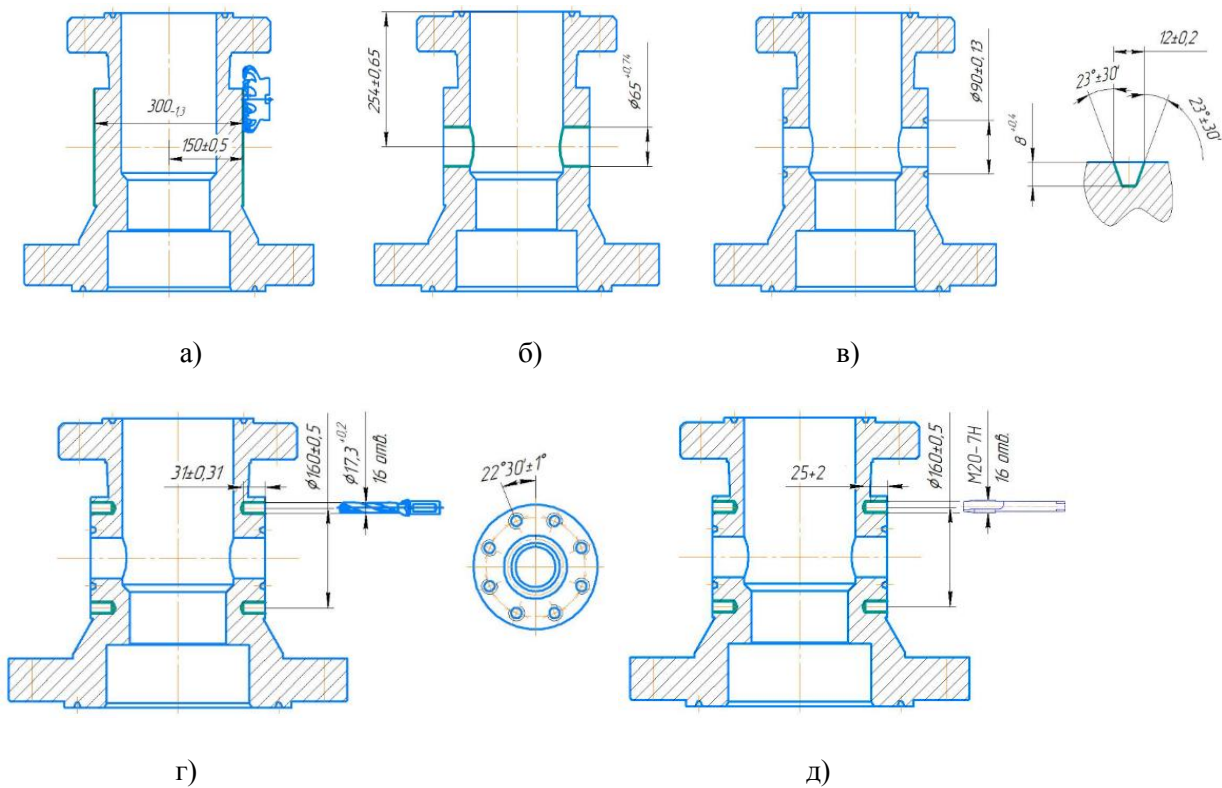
Технологический процесс обработки боковых фланцев корпусов (а – фрезерование боковых плоскостей, б – сверление отверстия Ø65, в – растачивание уплотнительной канавки Ø90, г - сверление 16 отверстий Ø17,3, д - нарезание резьбы М20-7Н в 16 отверстиях)
